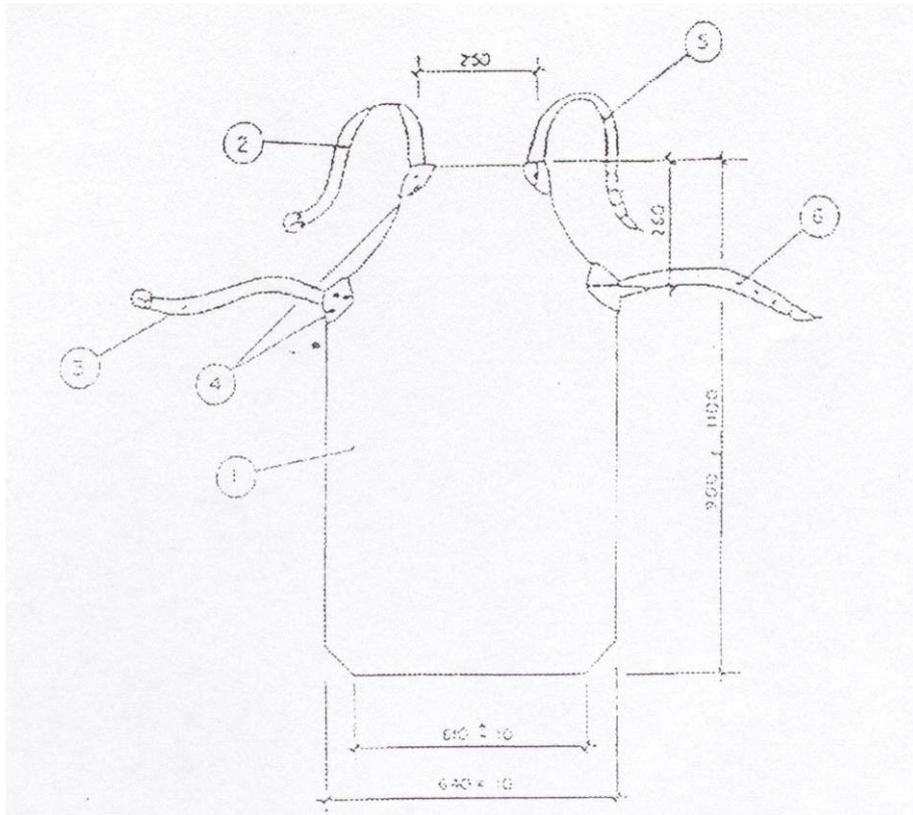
vii: Mandil de cuero para soldador
